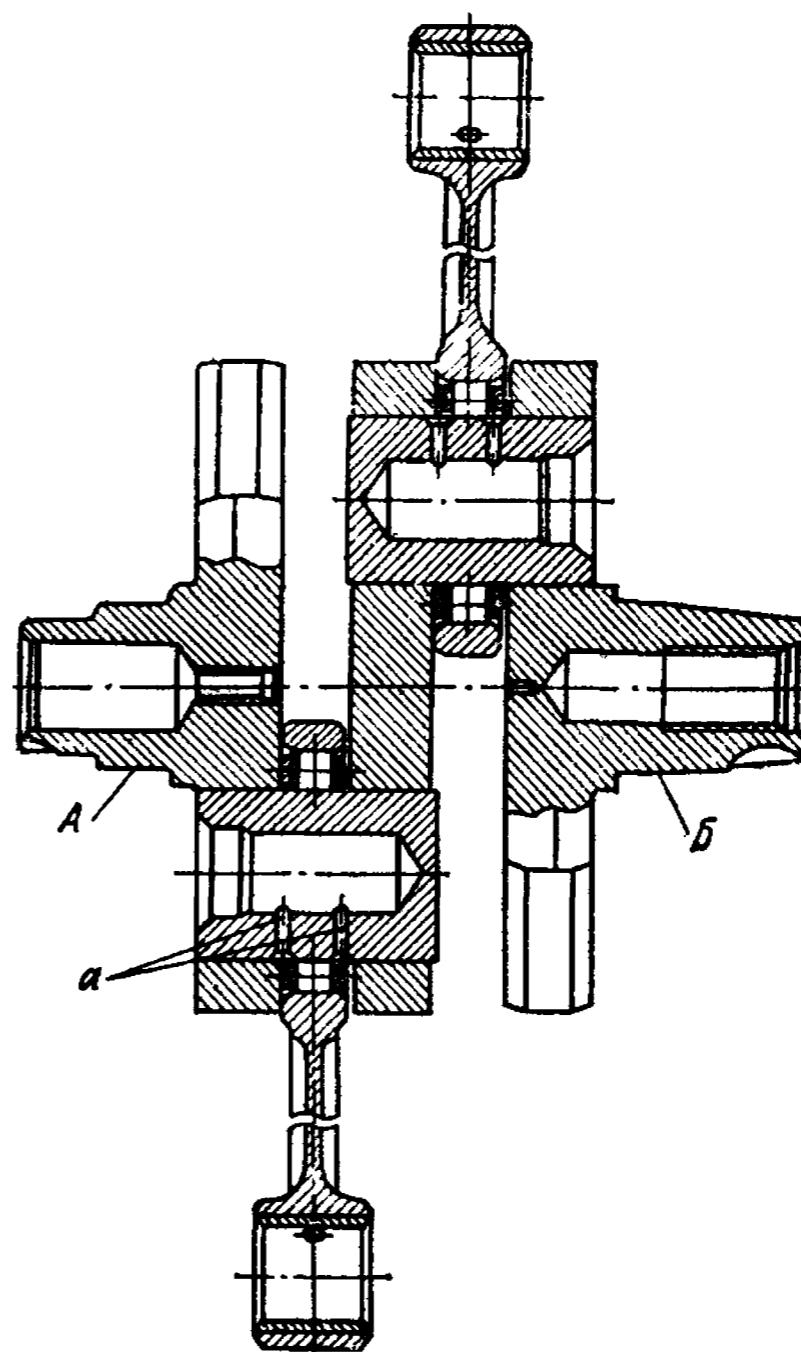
Расположение отверстий в пальцах кривошипного механизма при сборке с шатунами
